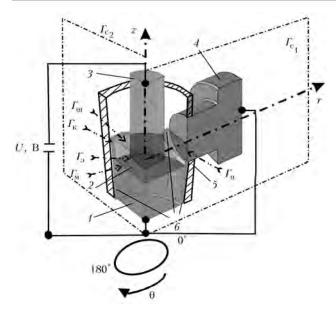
Схема граничных условий, принятых при решении задачи: 1- выплавленная часть заготовки; 2- шлаковая ванна; 3- расходуемый электрод; 4- приправляемый патрубок; 5- кристаллизатор; 6- гарнисаж
